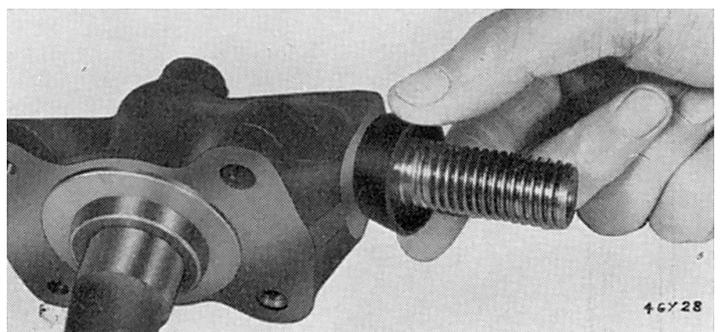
Montage du joint de caoutchouc au pivot de fusée
